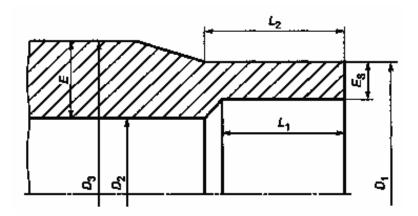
Размеры трубных концов деталей:  $D_1$  — средний наружный диаметр трубного конца;  $D_2$  — проходное сечение;  $D_3$  — средний наружный диаметр детали; E — толщина стенки детали в любом месте;  $E_s$  — толщина стенки в любом месте зоны сварки на максимальном расстоянии от торца детали;  $L_1$  — длина зоны сварки;  $L_2$  — длина трубного конца по наружной поверхности
